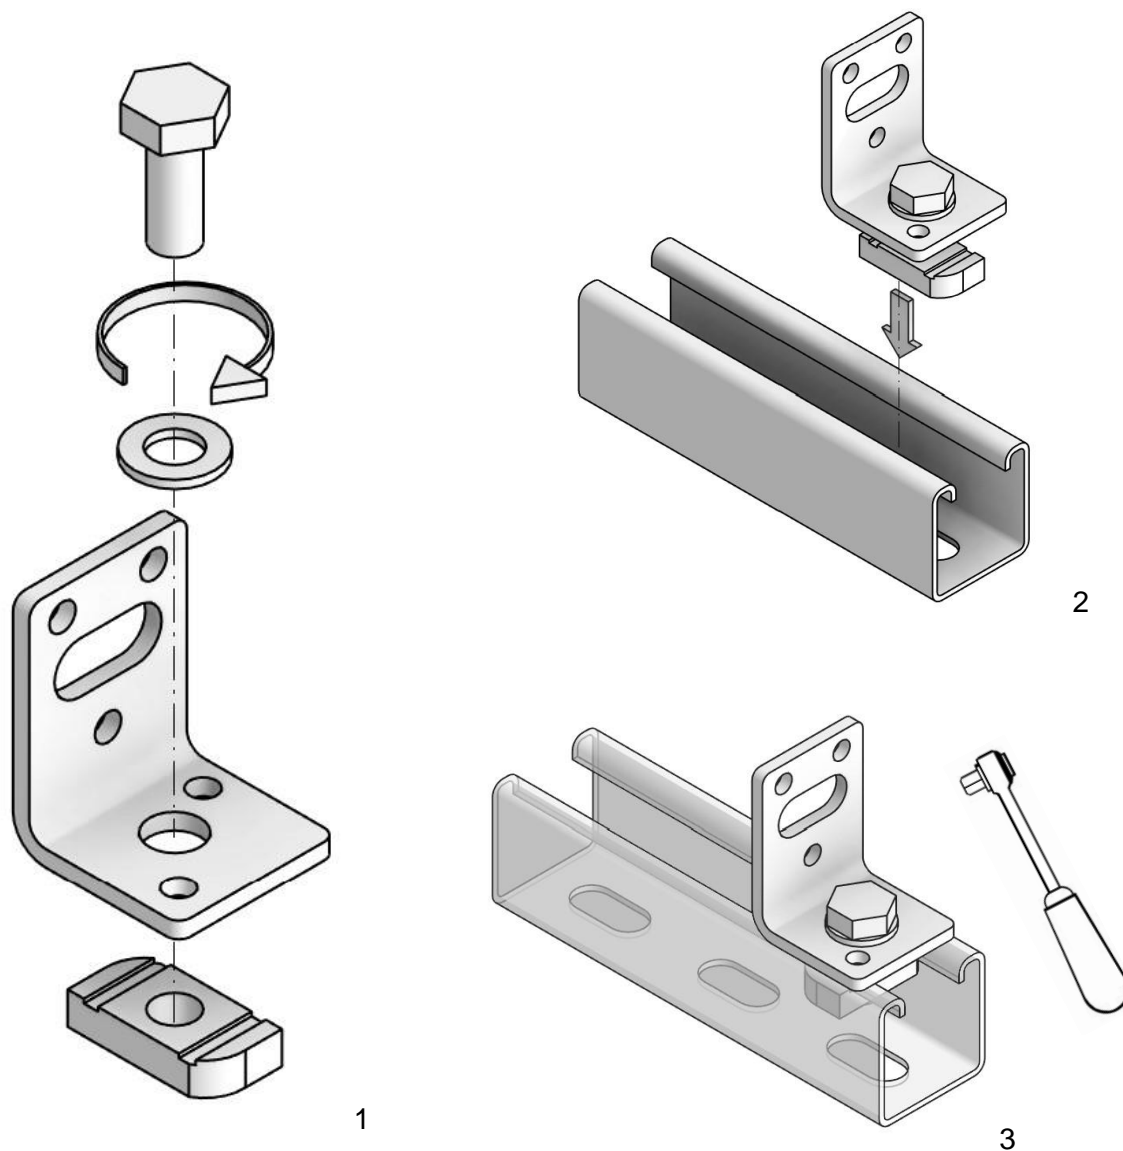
Крепление соединителя к профилю при помощи EFA 2
